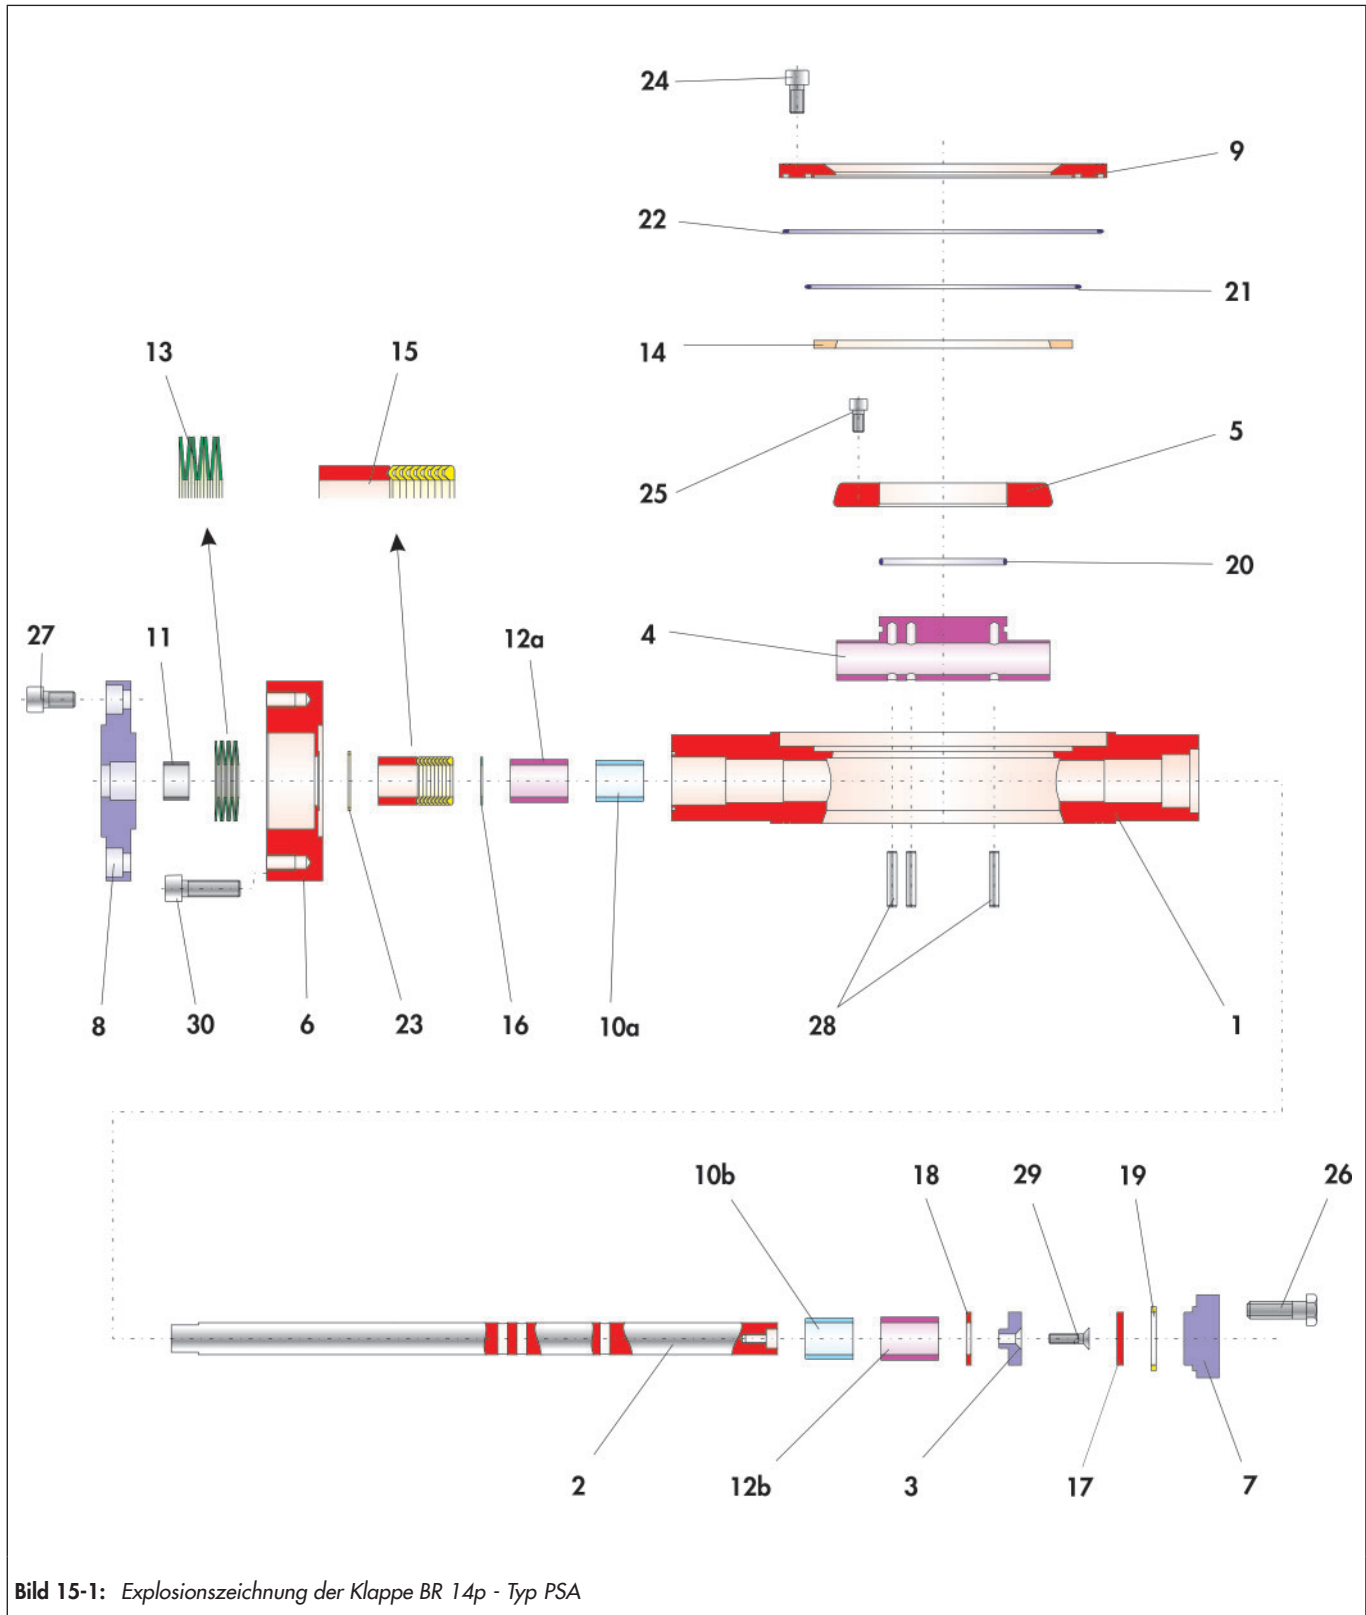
Explosionszeichnung der Klappe BR 14p - Typ PSA
